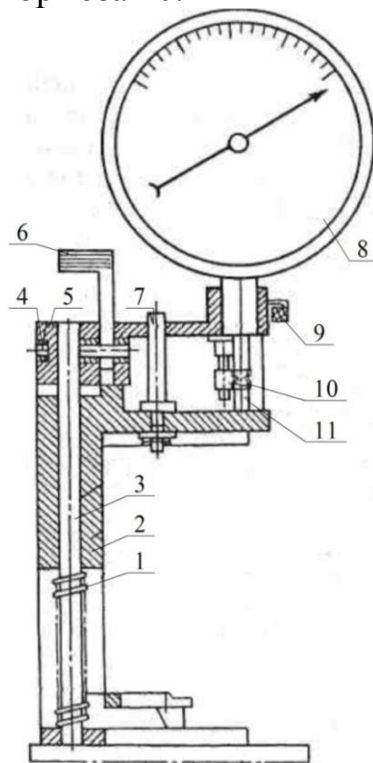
Приспособление для определения величины зазора КИ-9918
